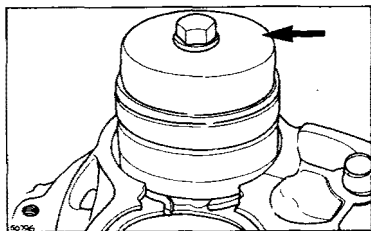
Запрессовка подшипников с помощью специального приспособления
